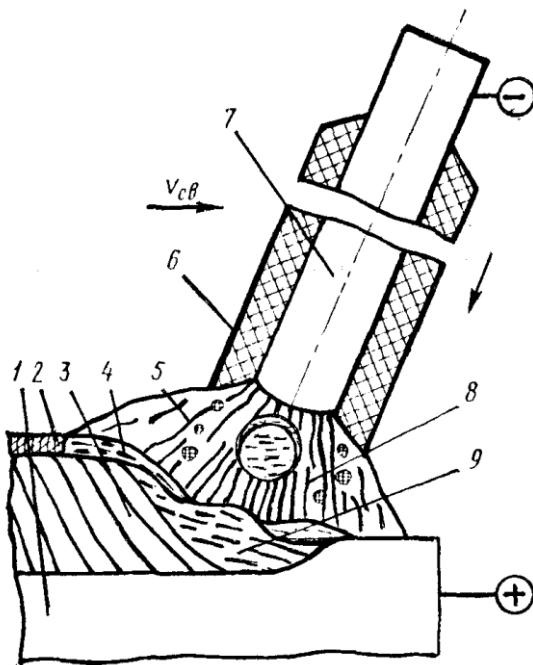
Схема процесса ручной электродуговой сварки металлическим покрытым электродом: 1 – основной металл; 2 – шлаковая корка; 3 – сварной шов; 4 – шлаковая ванна; 5 – газовая защитная атмосфера; 6 – покрытие электрода; 7 – стержень электрода; 8 – электрическая дуга; 9 – металлическая ванна
